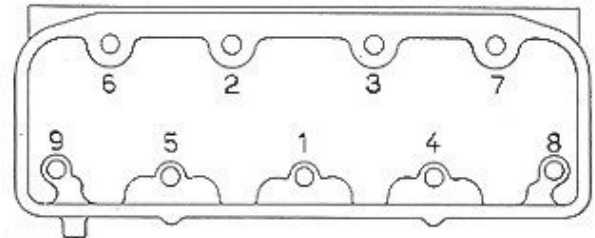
Schema der Anzugsreihenfolge der Befestigungsschrauben des Zylinderkopfes.
